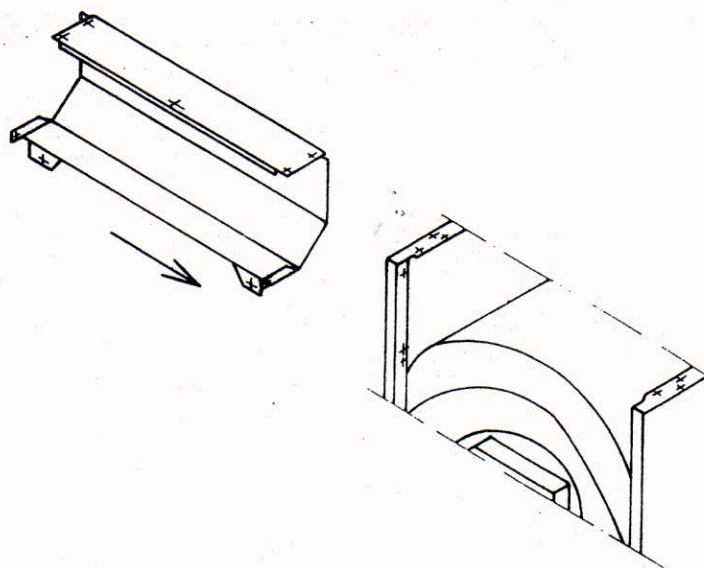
Montage Rückwandblech der Schaltfeldaufnahme
